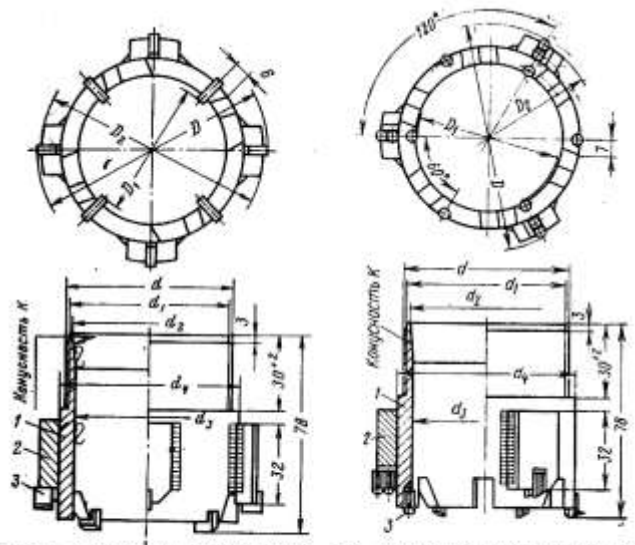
Твердосплавная коронка М1: 1 — корпус коронки; 2 — ребро; 3 — твердосплавная пластина
